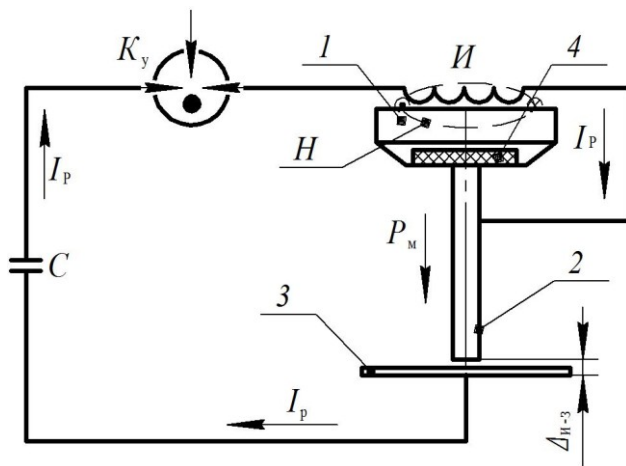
Разрядный контур устройства ВКС с ИДП:
